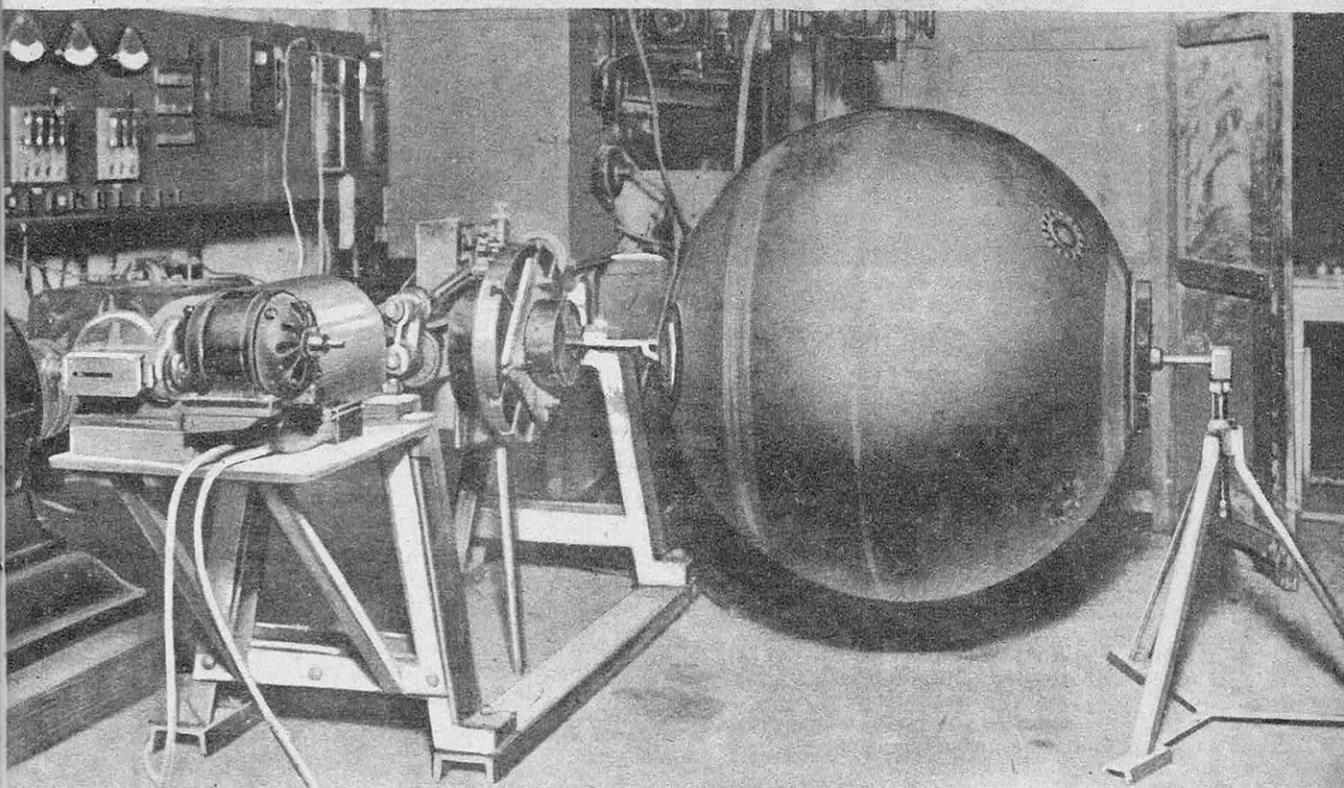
SOUDURE AUTOMATIQUE A L'ARC D'UN FLOTTEUR DE MARINE (LA SOUDURE AUTOGENE FRANÇAISE)
